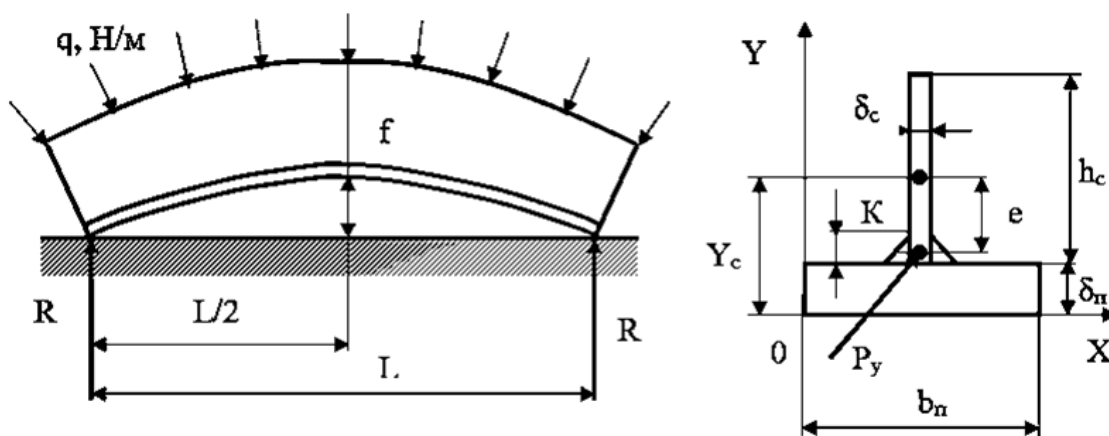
Розрахункова схема визначення зусиль притискання балки в кондукторі [29]
